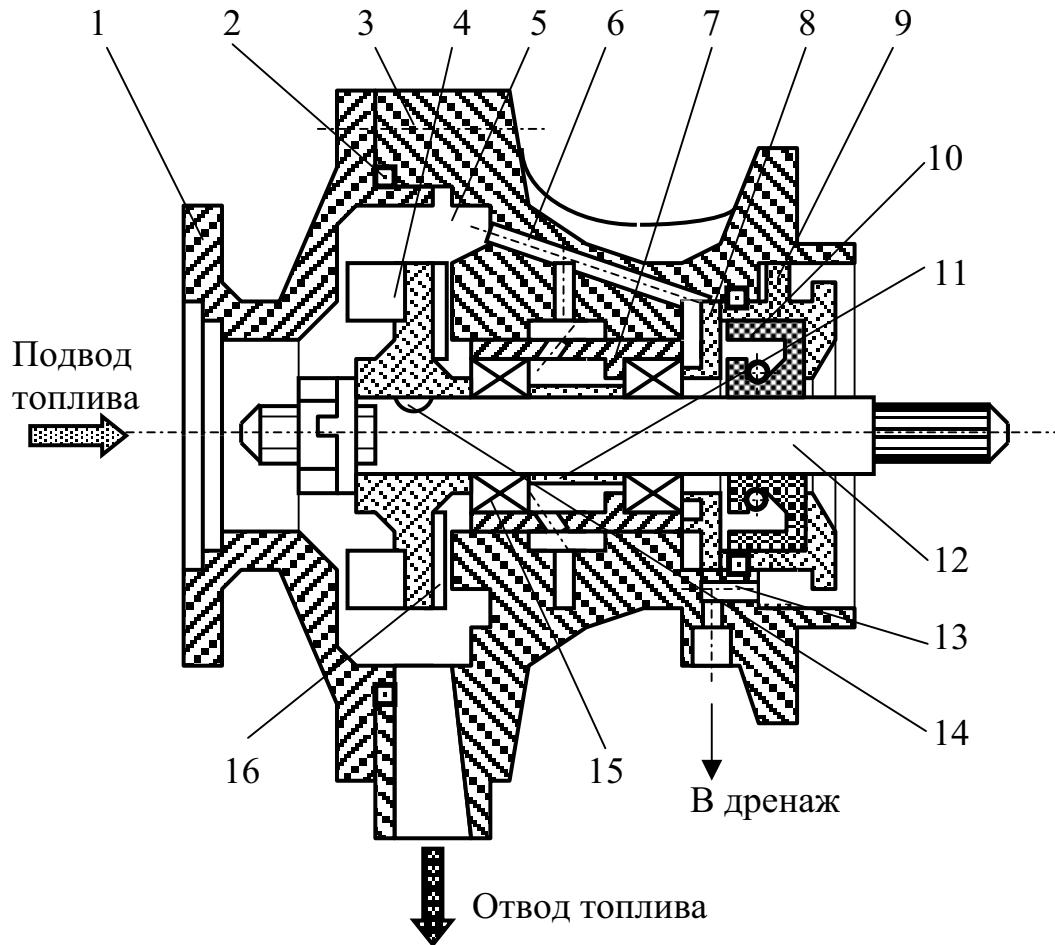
Подкачивающий центробежный насос ДЧН-70:
